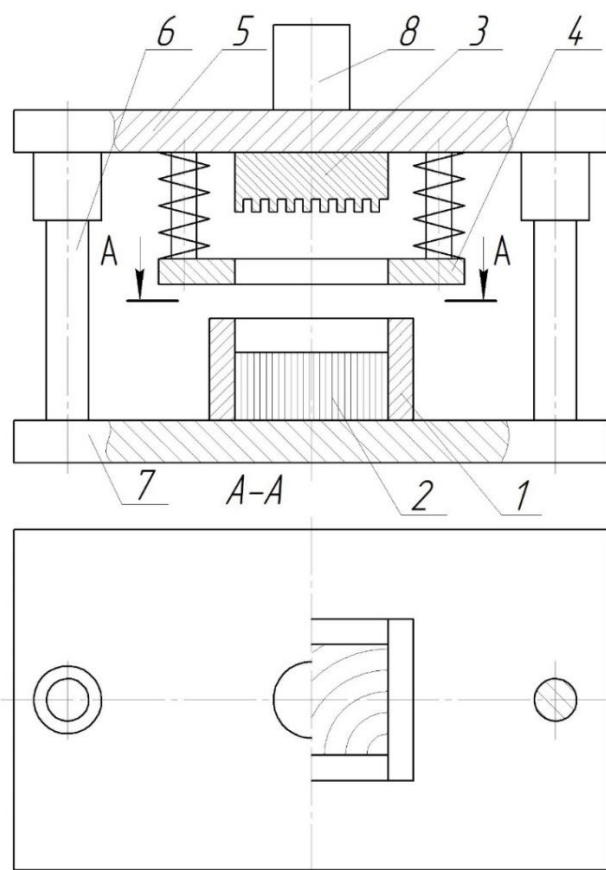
Схема приспособления для торцевого прессования прямоугольных шипов в древесине: 1 – матрица; 2 – заготовка; 3 – пуансон; 4 – подвижный съемник; 5 – верхняя плита; 6 – колонки; 7 – нижняя плита; 8 – хвостовик
